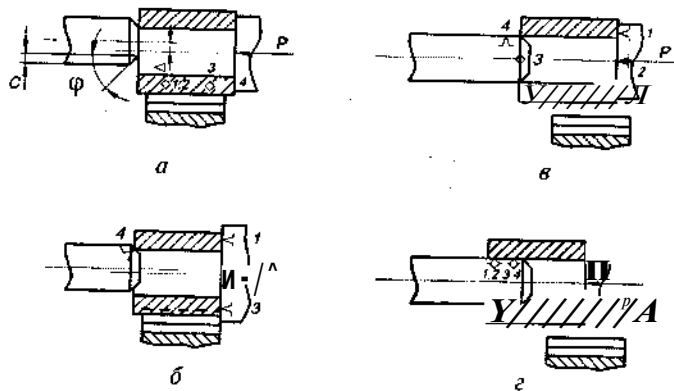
Различные положения при сборке деталей типа втулка—вал:
